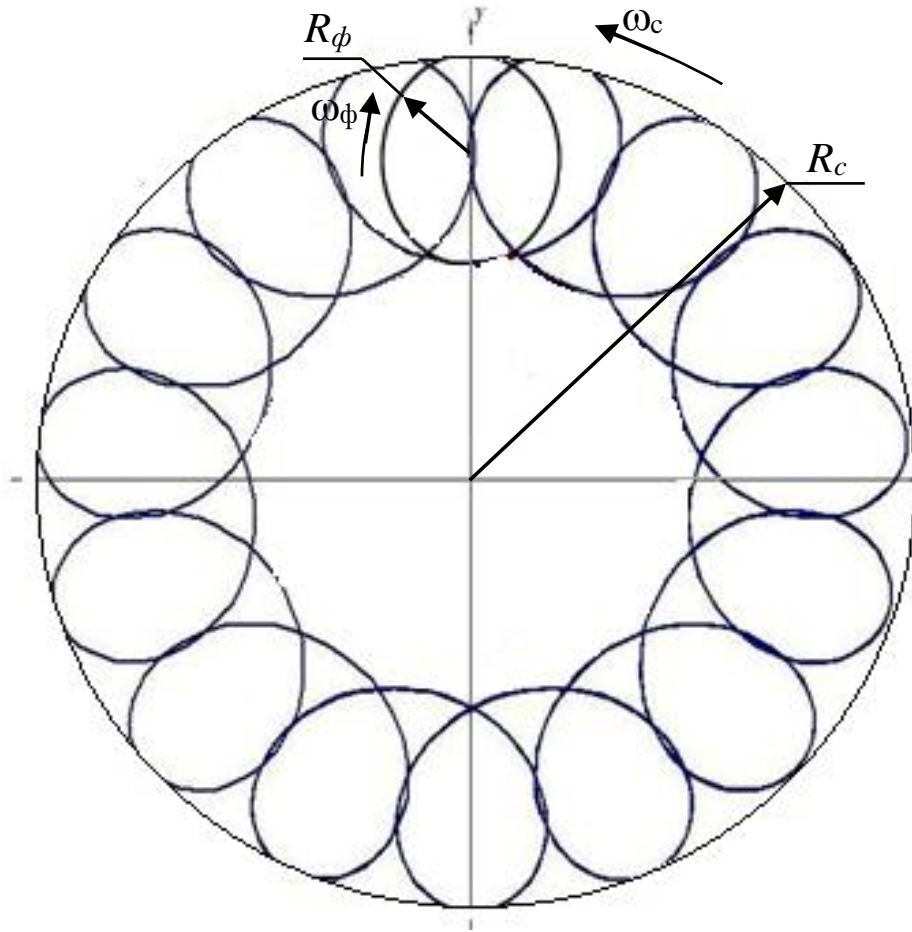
Траєкторія руху фрези при зустрічному фрезеруванні увігненого контуру
